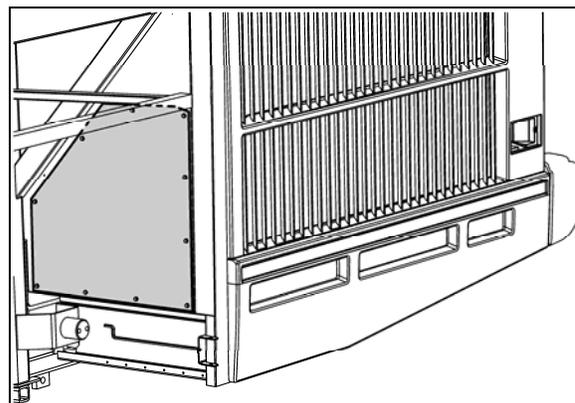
PANNEAU D'ACCÈS DERRIÈRE LA ROUE D'ESSIEU AUXILIAIRE
